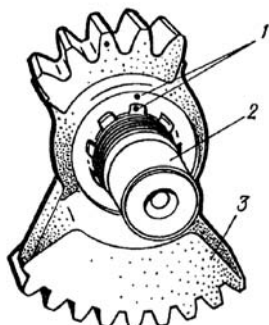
Совмещение меток при сборе сектора с валом. 1 — метки; 2 — поворотный вал; 3 — сектор.
